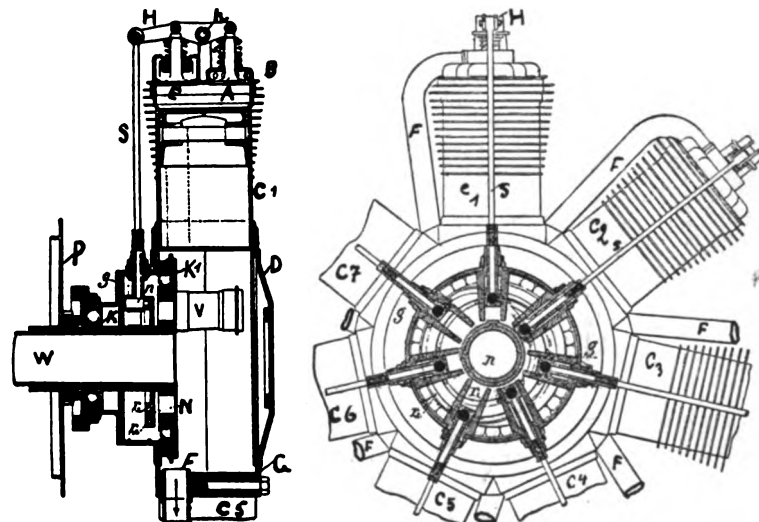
Schnittzeichnung des Umlaufmotors von Rossel-Peugeot. C_1 bis C_7 Zylinder. W Kurbelwelle mit V Kurbelzapfen. K, K_1 Kugellager. G Kurbelgehäuse. D Gehäusedeckel. g Gehäuse für die Steuerung. n Nutenscheibe für die Steuerung. S Ventilstangen. P Befestigungsflansch.
